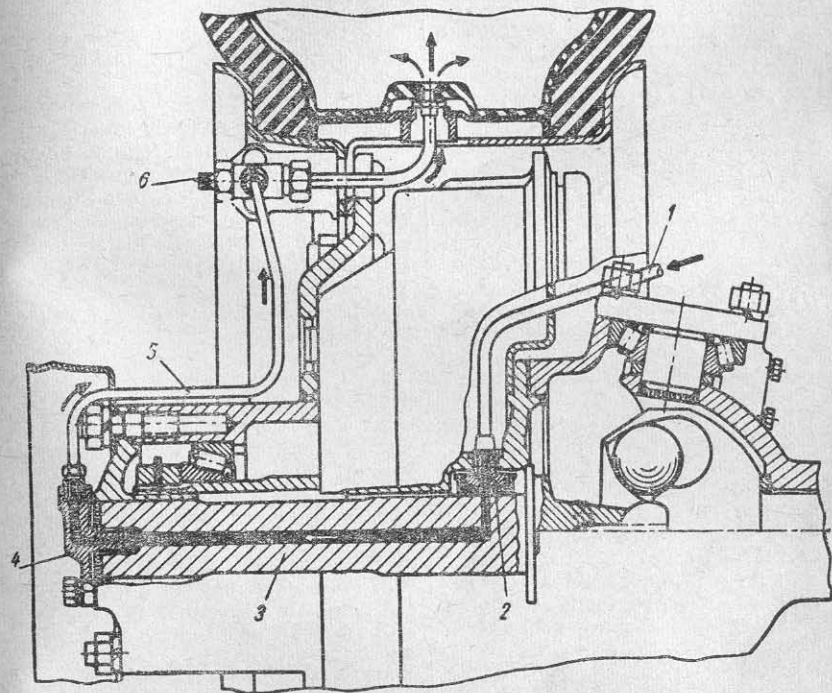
Схема подвода воздуха к шине переднего колеса:
